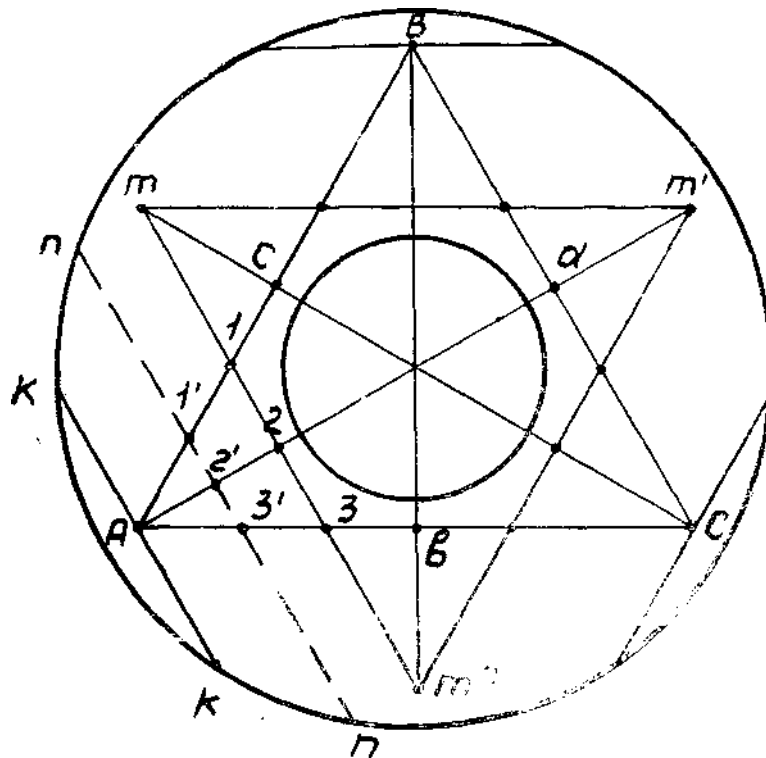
Схема контроля поверхности опорных кольцевых дисков
